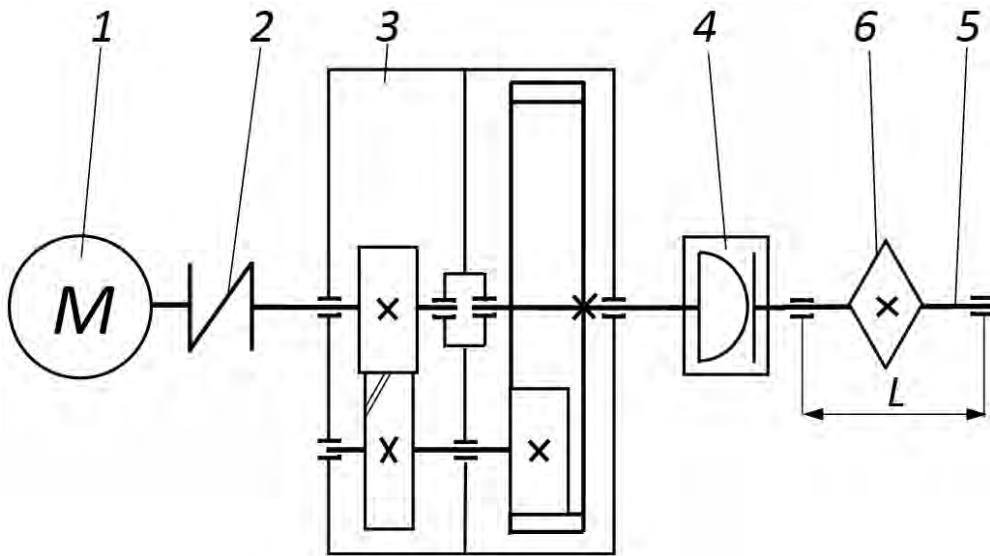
Схема привода скребкового конвейера (вид сверху): 1 – асинхронный электродвигатель; 2 – муфта упругая втулочно-пальцевая; 3 – редуктор двухступенчатый соосный (первая ступень – косозубая цилиндрическая, вторая – прямозубая цилиндрическая с внутренним зацеплением); 4 – муфта компенсирующая жесткая кулачково-дисковая; 5 – приводной вал; 6 – приводная звездочка
